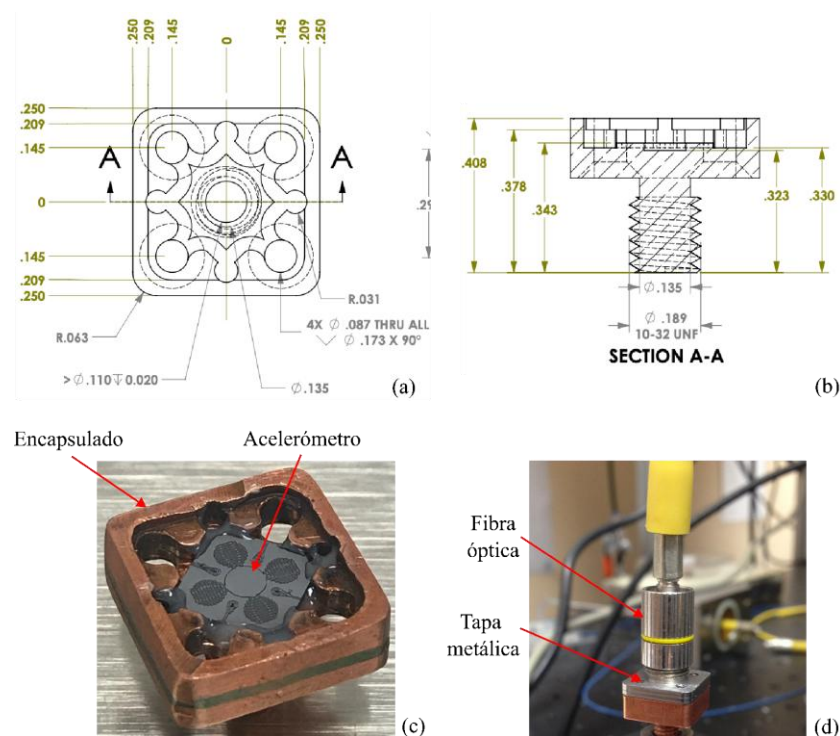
Encapsulado para acelerómetro MOEMS [8]. (a) Dimensiones de cara superior del encapsulado en pulgadas; (b) Sección transversal del encapsulado; (c) Acelerómetro y encapsulado fabricados; (d) Encapsulado de cobre con tapa metálica y fibra óptica.
